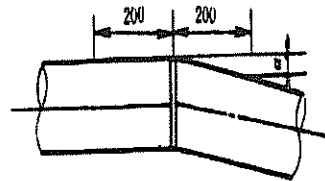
管道焊接角变形折口偏差示意图
